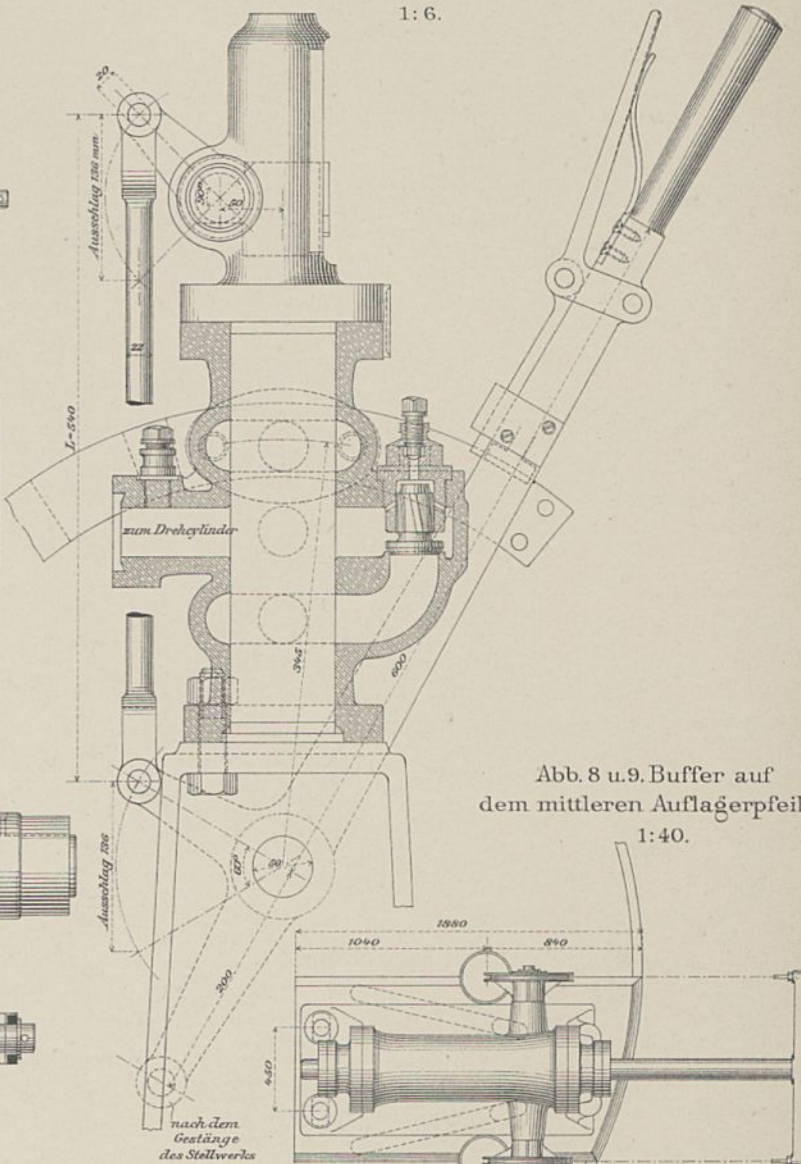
Lothrechter Schnitt rechtwinklig zur Brückenlängsachse durch die Steuervorrichtung des Hebecylinders u. des Cylinders zum Schliessen der Brücke. 1:6.
